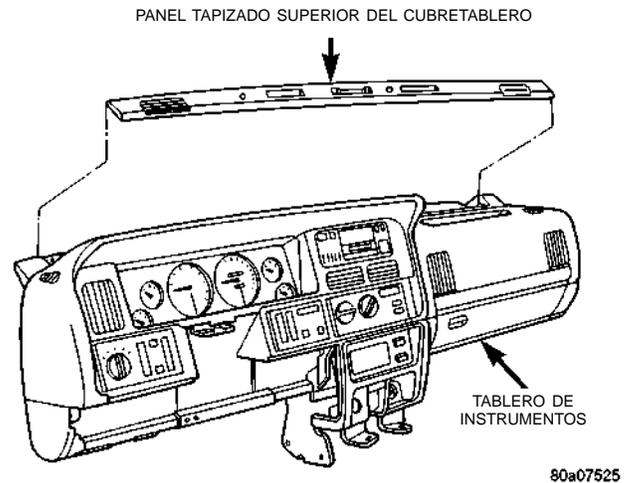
Desmontaje/instalación del panel tapizado superior del cubretablero
